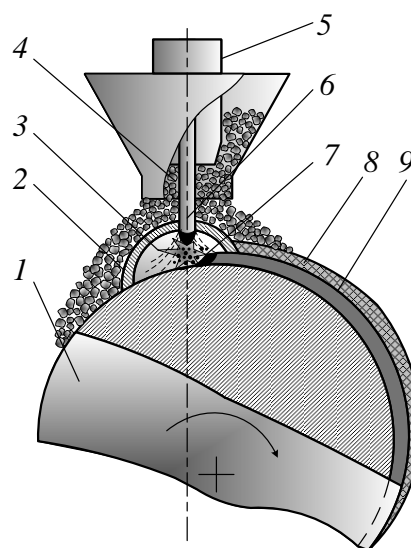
Схема автоматической наплавки под слоем флюса:
